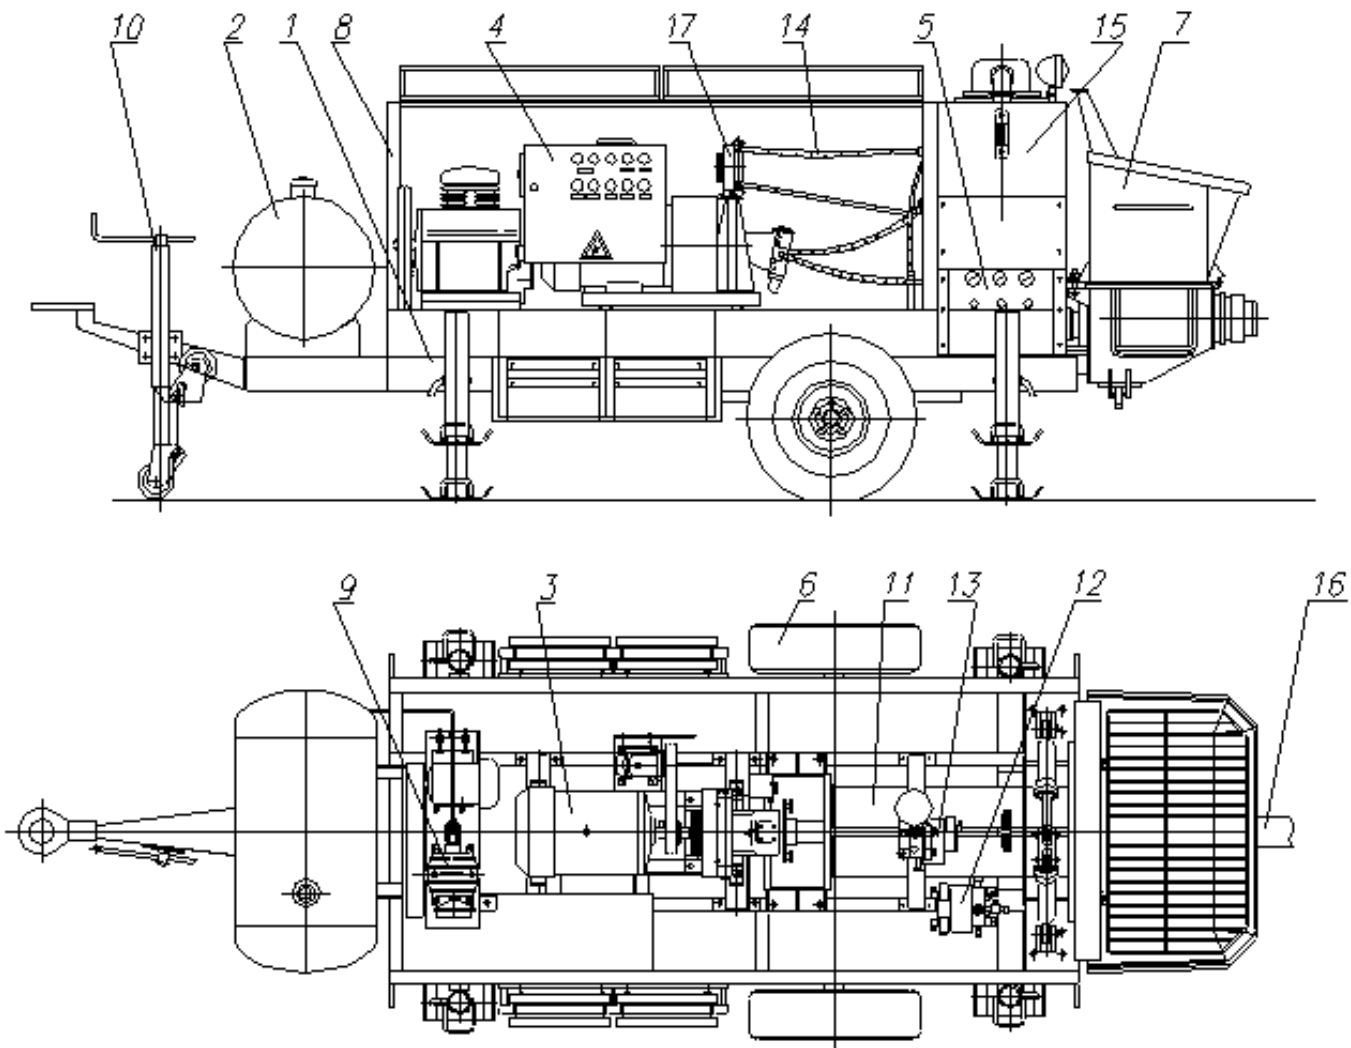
Бетононасос СБ-207: 1 – рама; 2 – водобак; 3 – привод гидронасосов; 4 – пульт управления; 5 – панель контроля; 6 – установка колес; 7 – воронка приемная; 8 – кожух; 9 – установка компрессора; 10 – дышло; 11 – цилиндропоршневая группа; 12 – блок управления 1; 13 – блок управления 2; 14 – гидросистема; 15 – гидробак; 16 – комплект бетононасосов; 17 – маслоохладитель.
